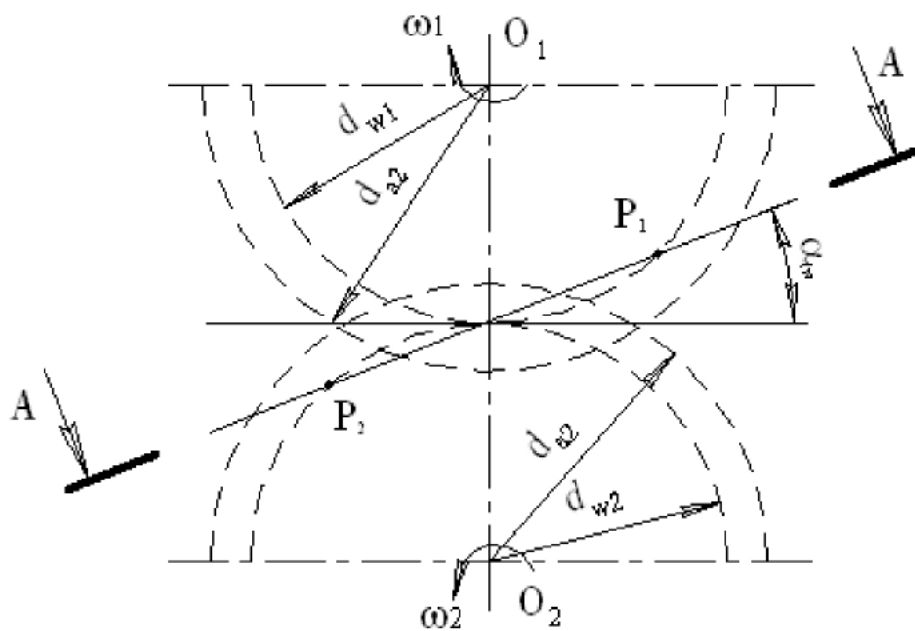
Схема возникновения многопарного зацепления в цилиндрической зубчатой передаче
